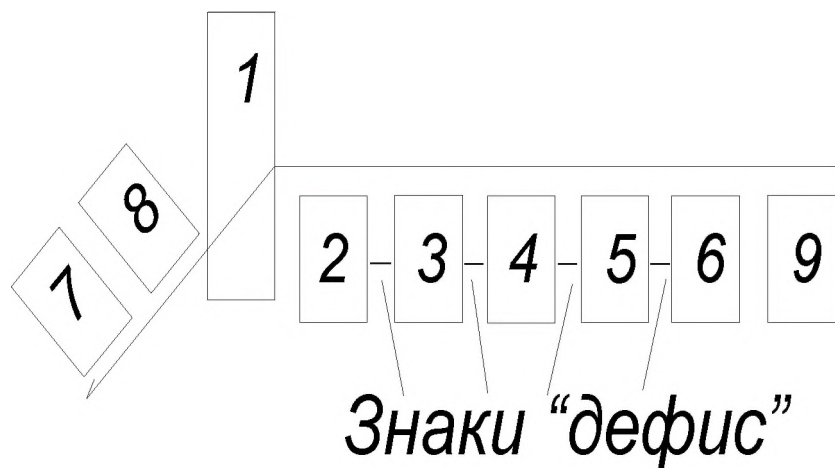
Условное обозначение сварного шва
